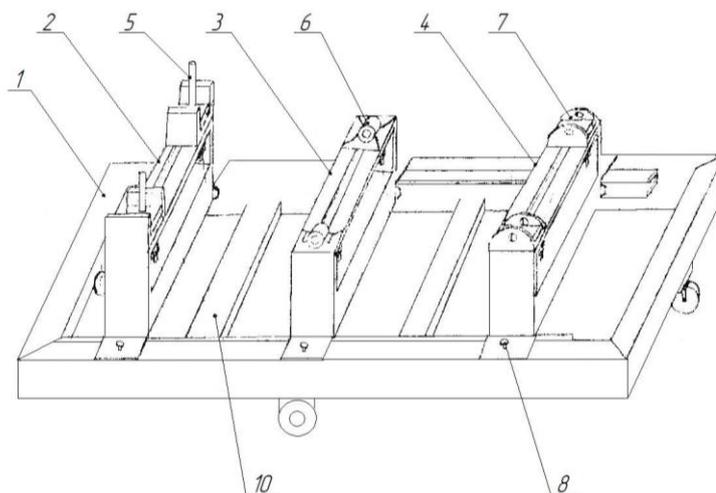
Универсальный стенд-кондуктор для разборки (сборки) кузовов легковых автомобилей
